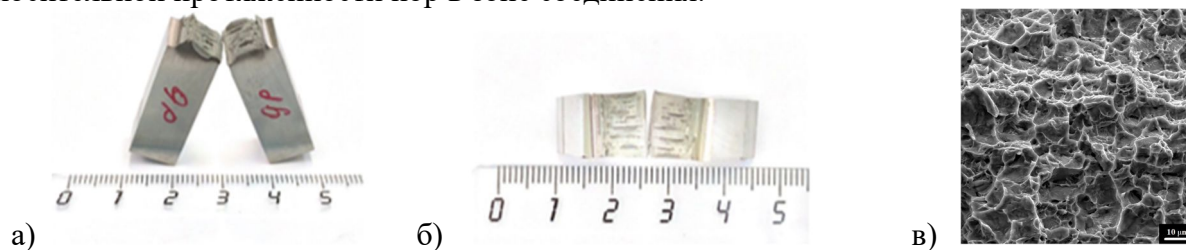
внешний вид образцов после испытаний на ударный изгиб (а) и поверхность излома образца (б, в)
